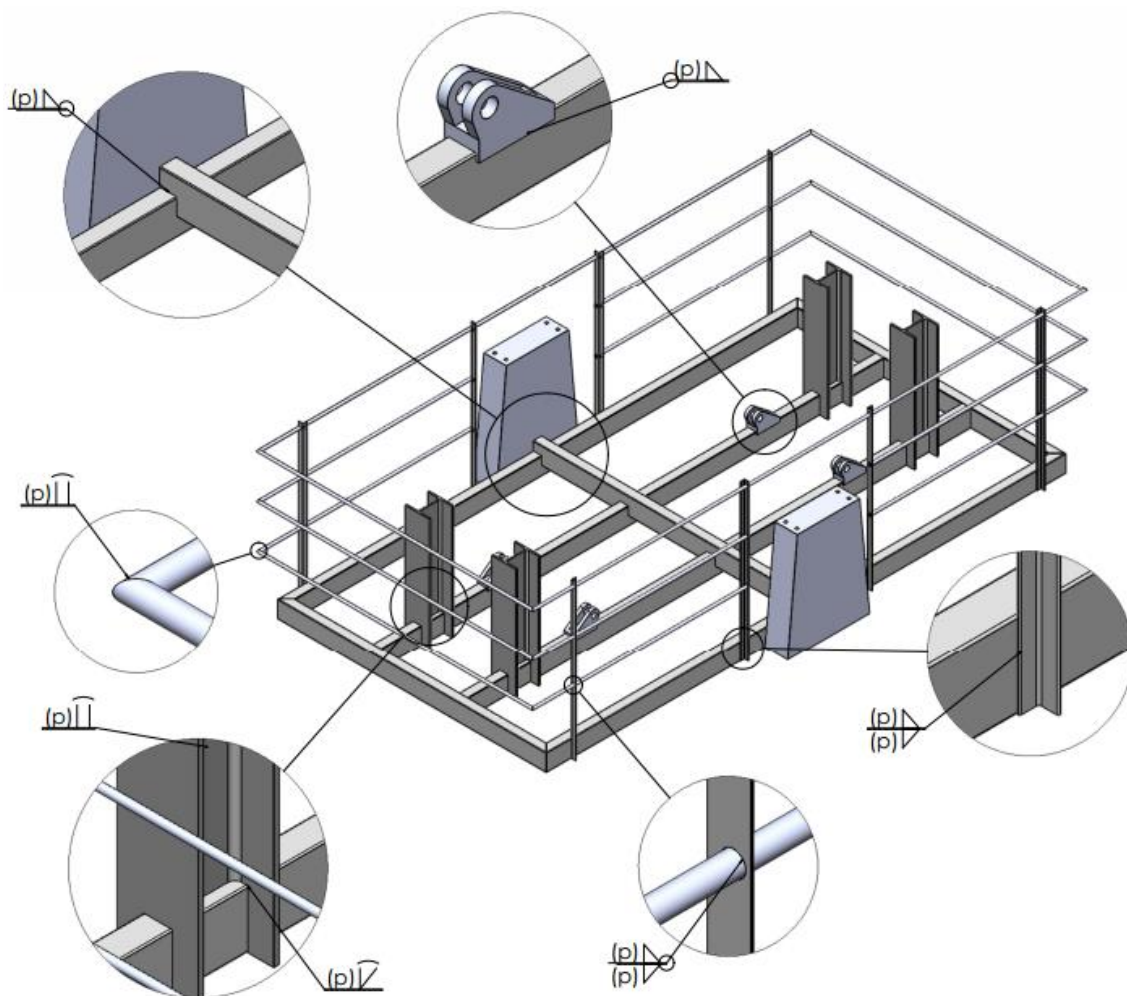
Simbologia para soldadura dos componentes da base.
